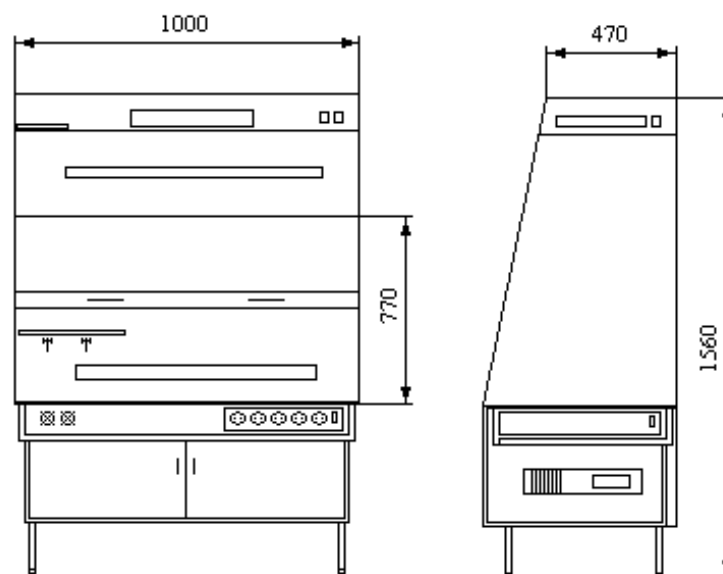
Витяжна шафа для виготовлення печатних плат
